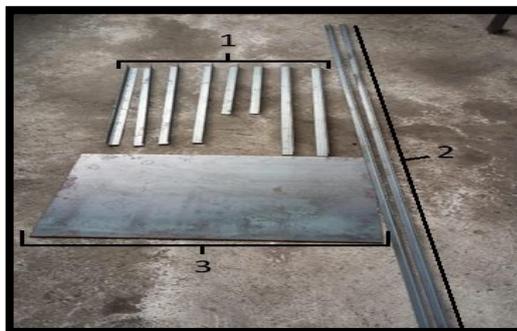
Materiales para la construcción del banco de soldadura MIG.
